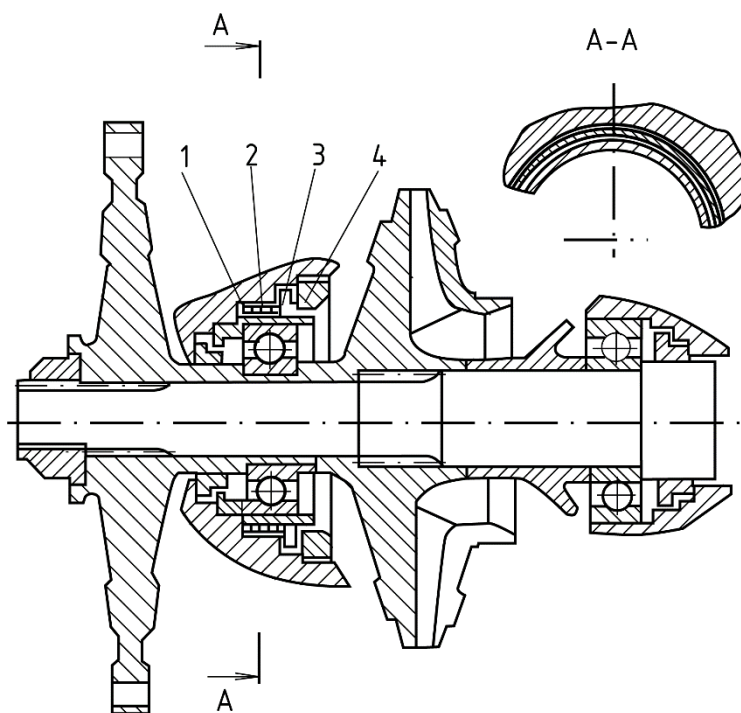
Упруго-демпферная опора ТНА с кольцом Аллисона:
